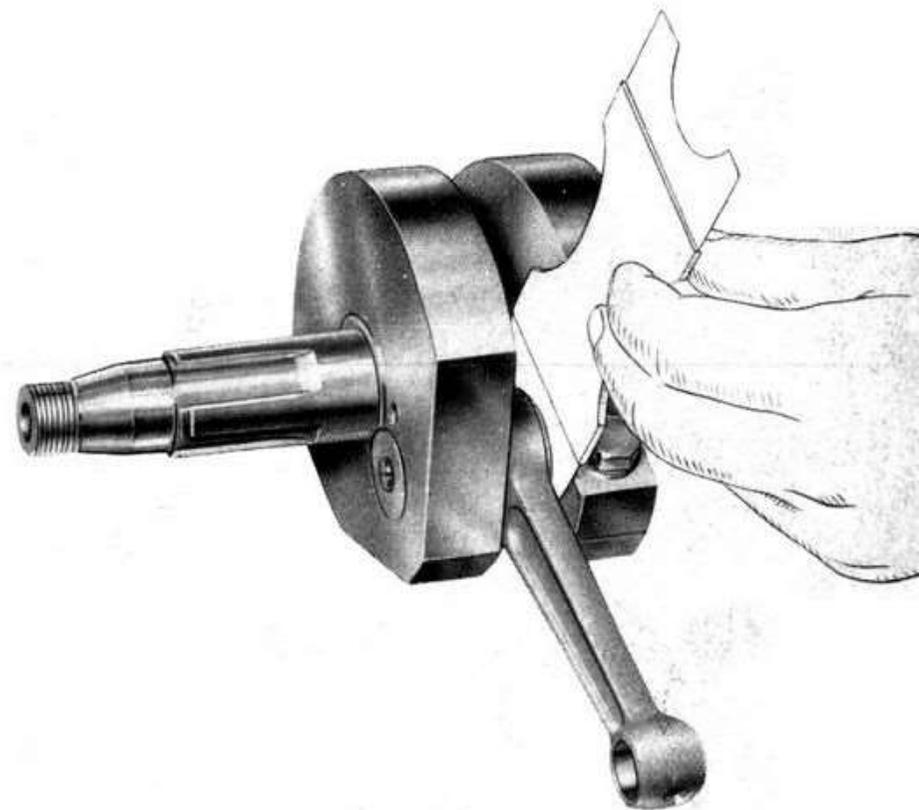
Controllo del giuoco di montaggio fra biella ed albero motore.
